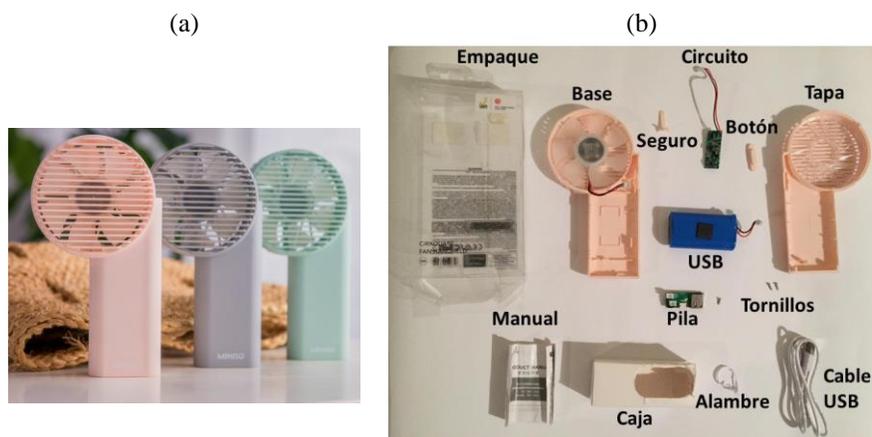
(a) producto terminado y (b) componentes que conforman el ensamble del ventilador
